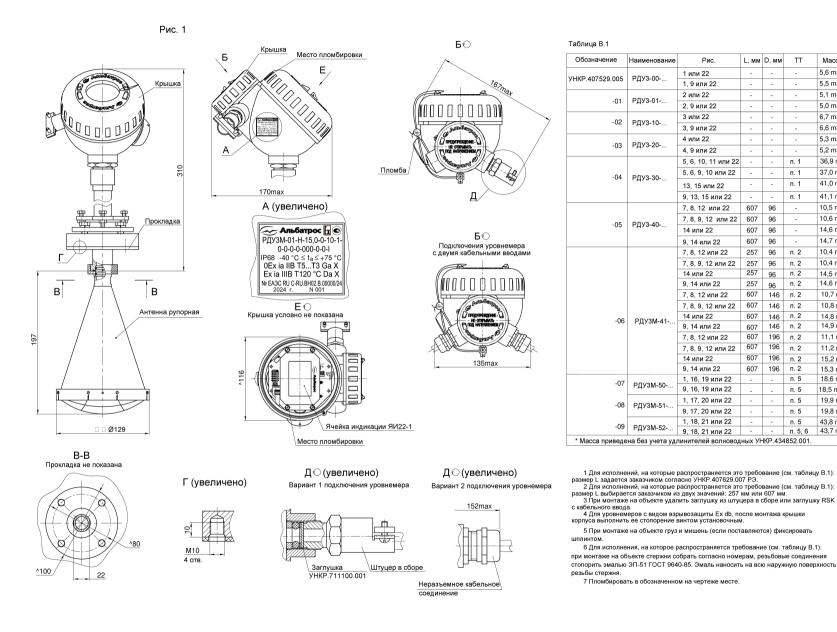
Габаритные размеры ПП (лист 1)
